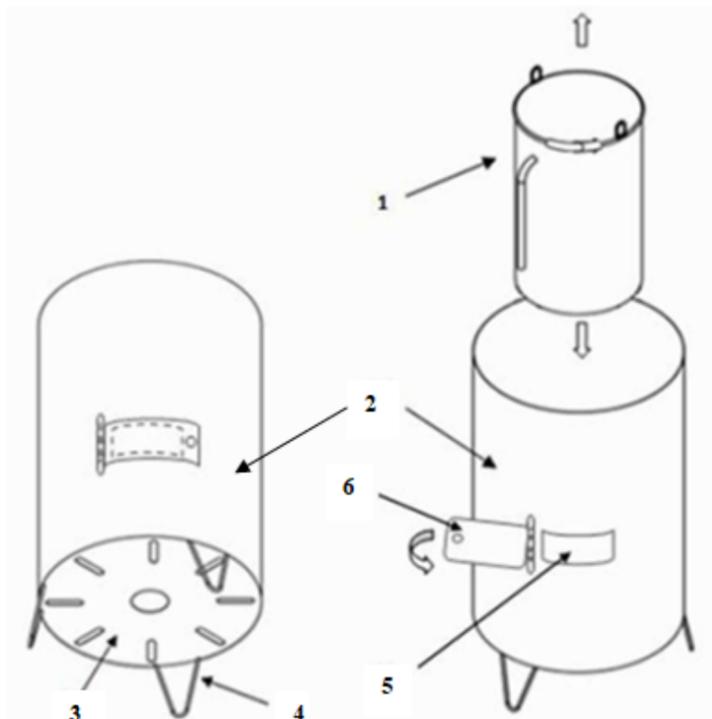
Desenho de conjunto. O reator (1) pode ser colocado ou retirado do tambor carcaça (2) que apresenta: grelha (3), pés (4), janela de inspeção (5) e portinhola para inspeção (6).
